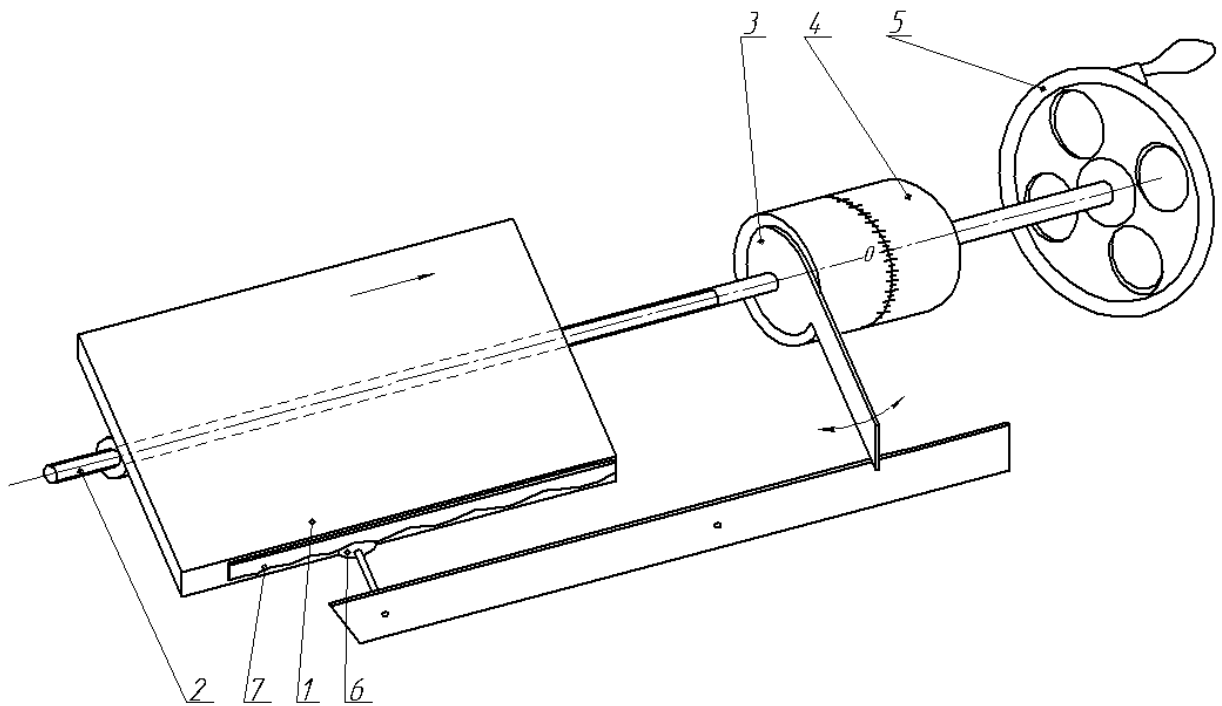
Стол координатно-расточного станка с корректирующей линейкой:
